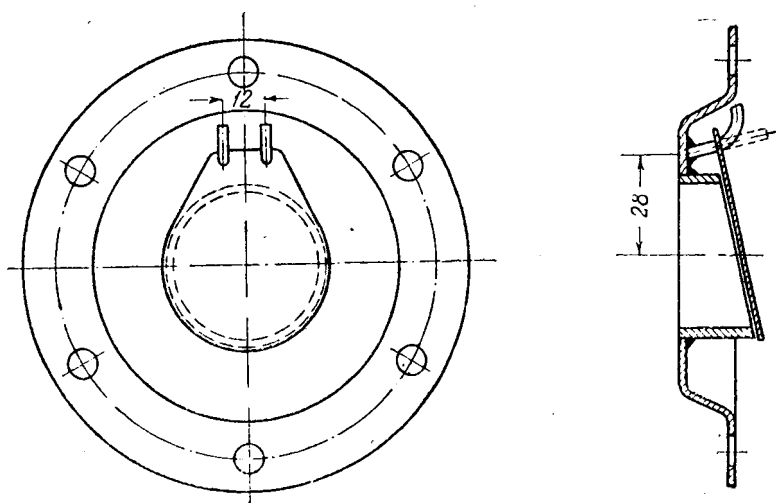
Верхняя часть бункера и корпуса газогенератора Г-14.
